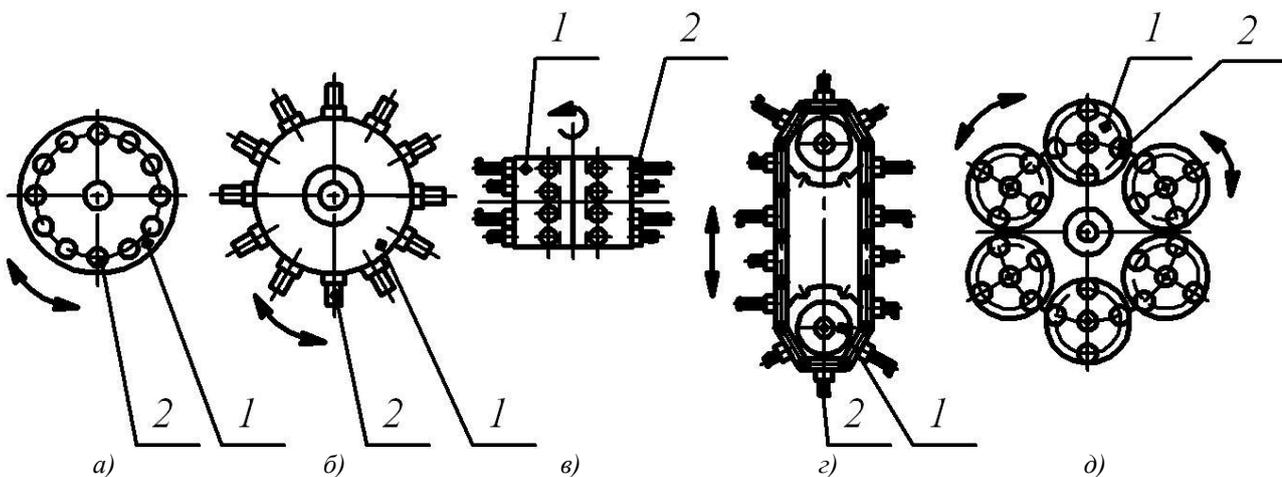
Схемы инструментальных магазинов (буквами обозначен тип исполнения магазина): а, б – дисковый; в – барабанный; г – цепной; д – планетарный
